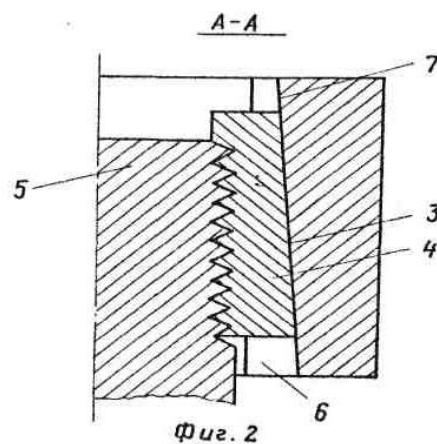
Пристрій для викручування шпильок: 1- корпус; 2-механізм захвата; 3- зовнішня поверхня; 4- губки; 6- пази; 7-опорна конічна поверхня.
